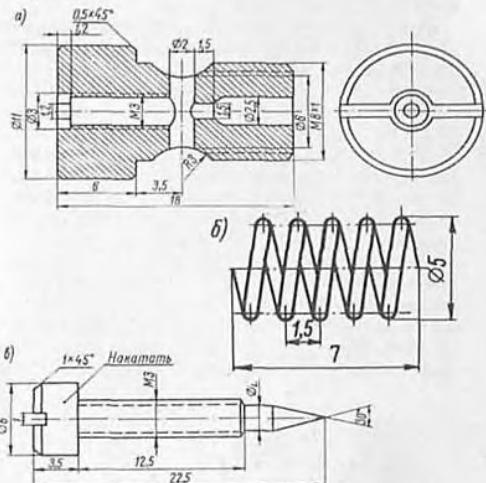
Устройство, регулирующее воздушный жиклер системы холостого хода: а — корпус; б — пружина; в — регулировочный винт.
